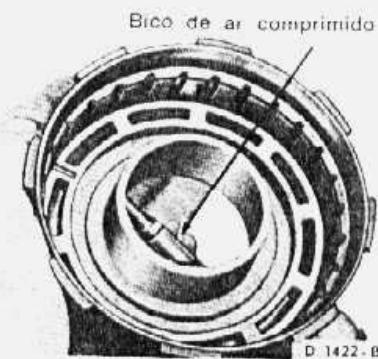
remoção do êmbolo da embreagem de ré-alta
